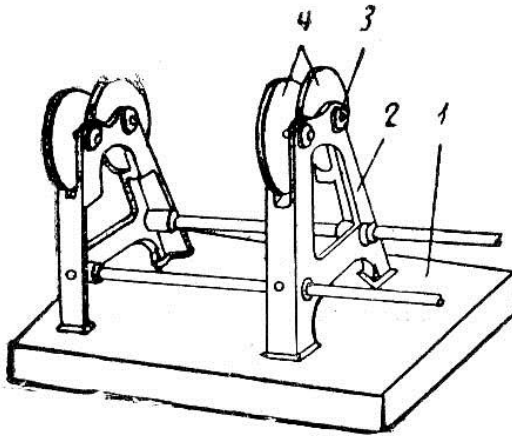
Пристрій для балансування робочих коліс на роликах:
